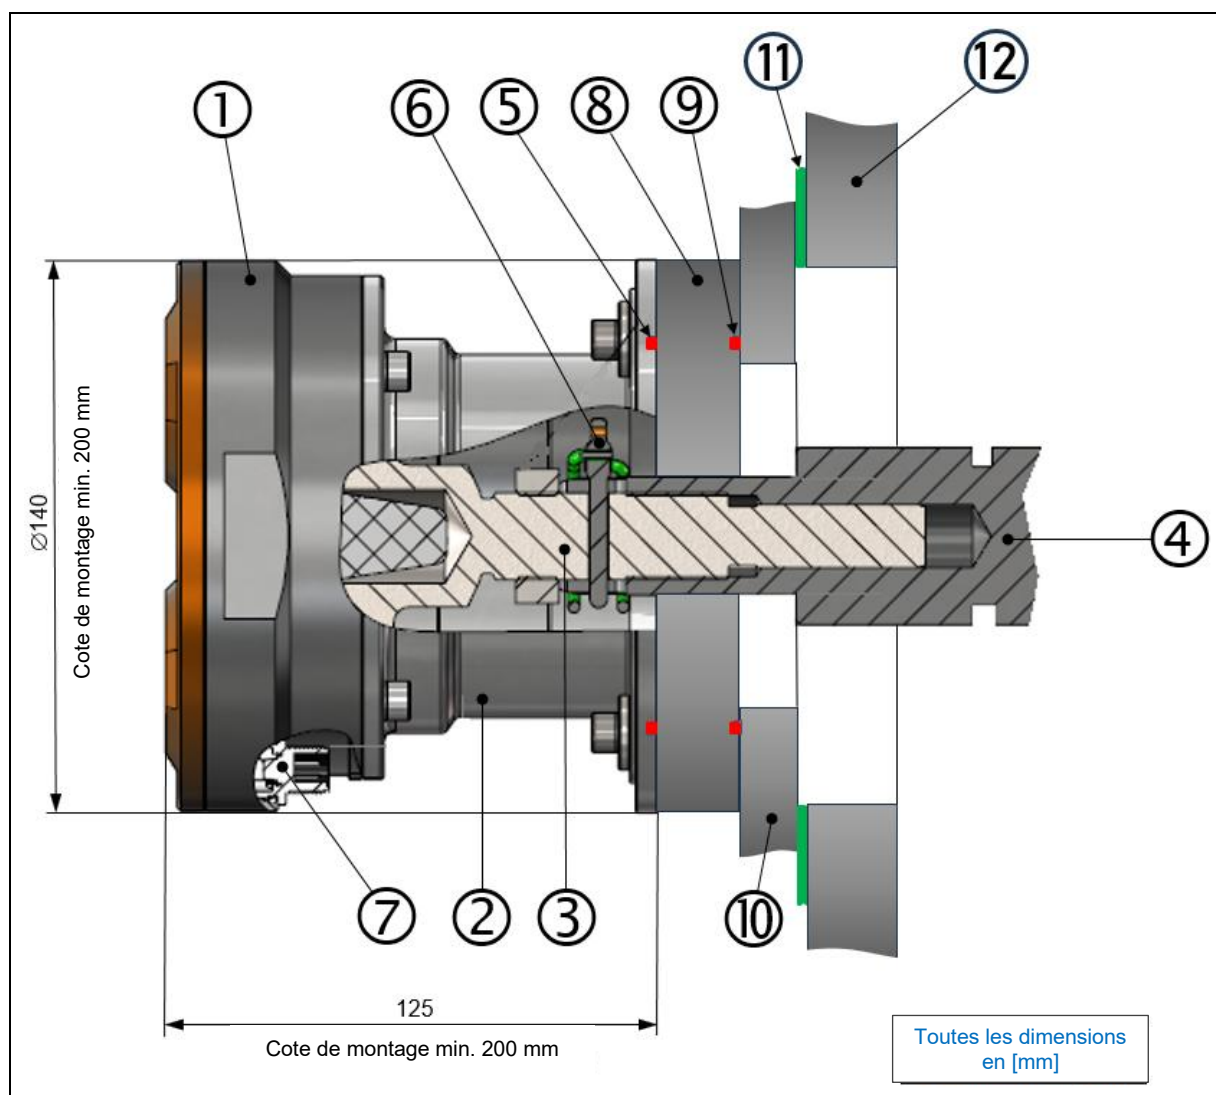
Vue d'ensemble complète des composants, BEAROMOS® 2020
